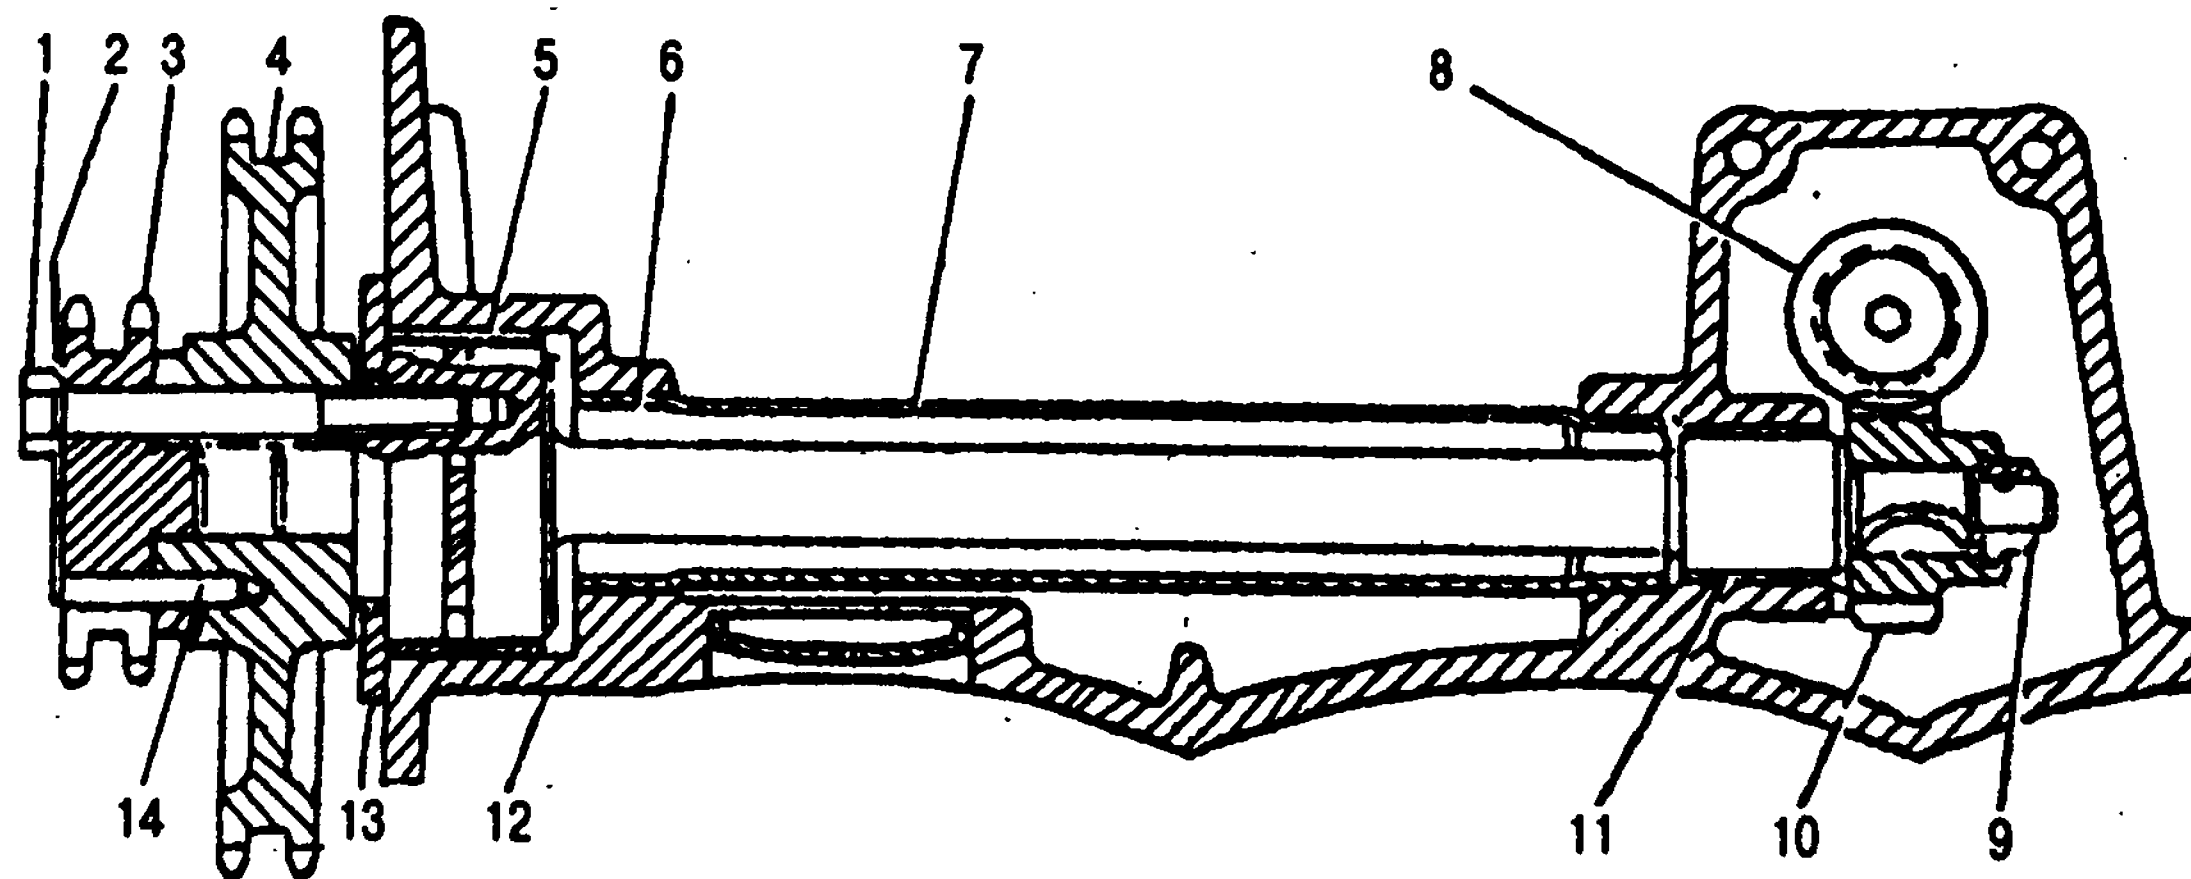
Промежуточный вал: 1 - болт; 2 - стопорная пластина; 3 - ведущая звездочка; 4 - ведомая звездочка; 5 - передняя втулка вала; 6 - промежуточный вал; 7 - труба промежуточного вала; 8 - шестерня ведомая привода масляного насоса; 9 - гайка; 10 - шестерня ведущая привода масляного насоса; 11 - задняя втулка вала; 12 - блок цилиндров; 13 - фланец промежуточного вала; 14 - штифт
